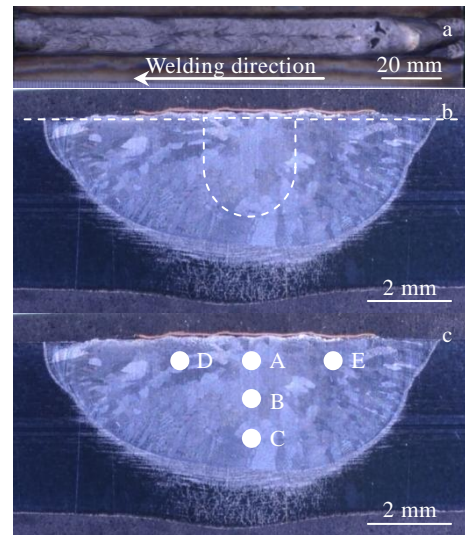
激光热丝焊后焊缝表面和截面形貌
